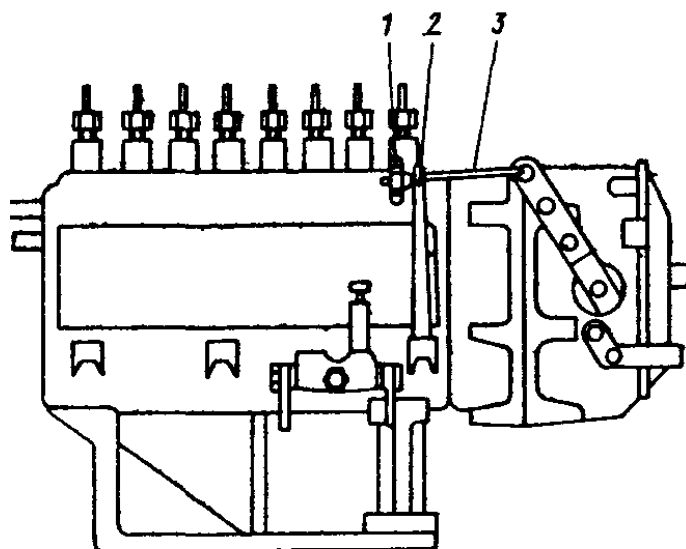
Крепление рычага регулятора топливного насоса двигателей ЯМЗ-238 при испытаниях:
